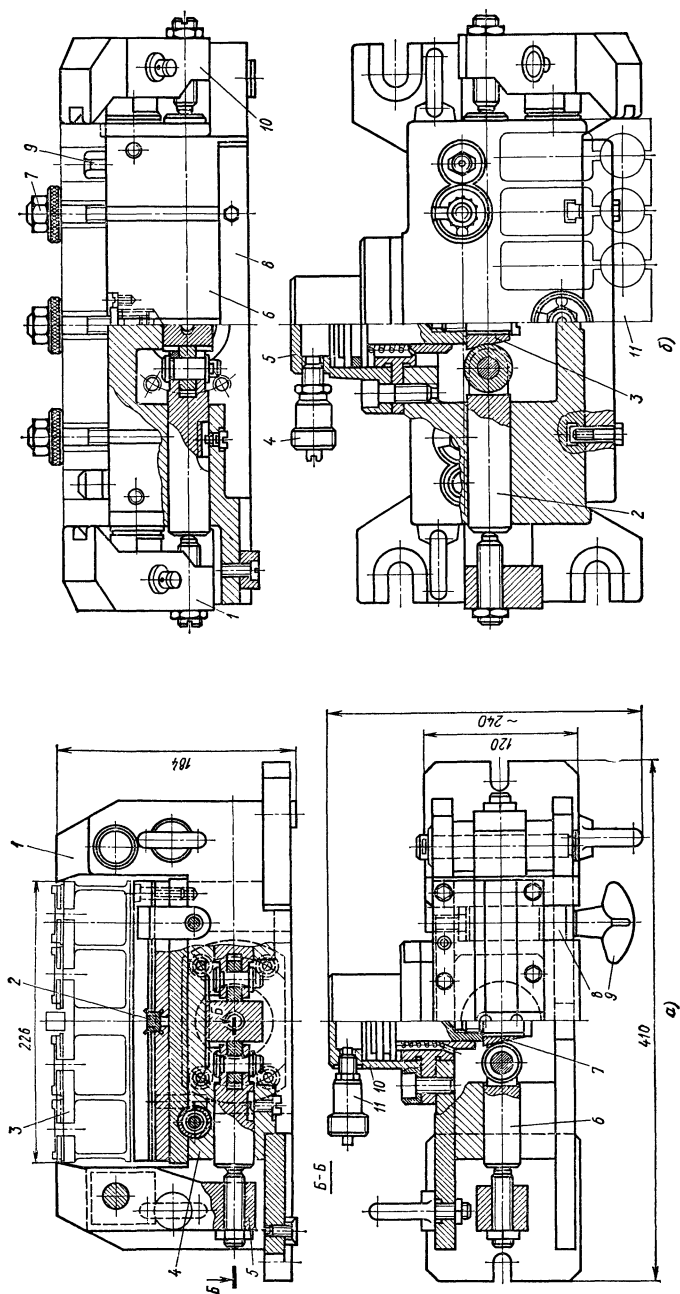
Специализированное наладочное приспособление кассетного типа для фрезерования деталей типа валов и втулок:
